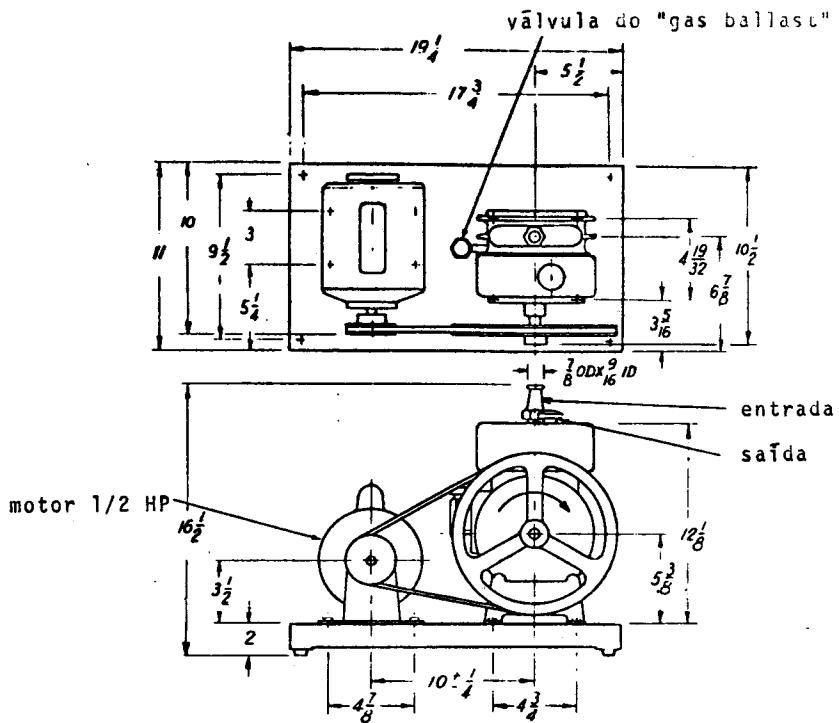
Desenho de Bomba Mecânica, marca Welch 1405 (USA) usada no laborat6rio didático (dimens6es em polegadas)
